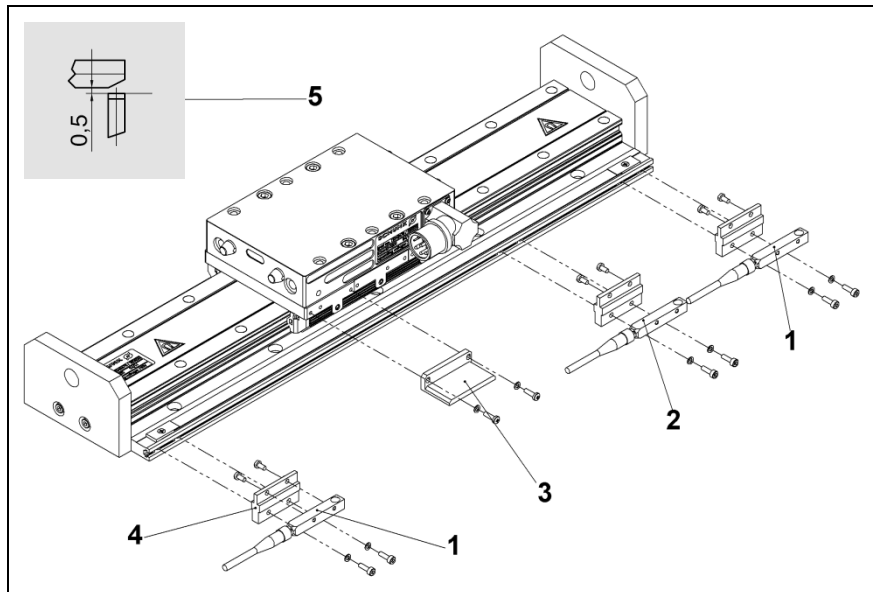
Endschalter mechanisch und Referenzschalter induktiv
